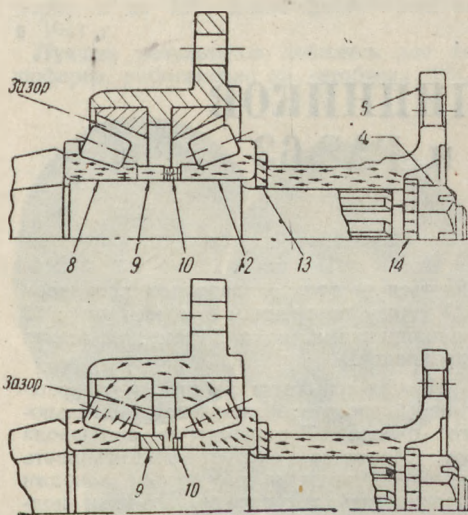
Схема передачи осевых усилий от гайки 4 при неправильной регулировке подшипников ведущей шестерни заднего моста:
